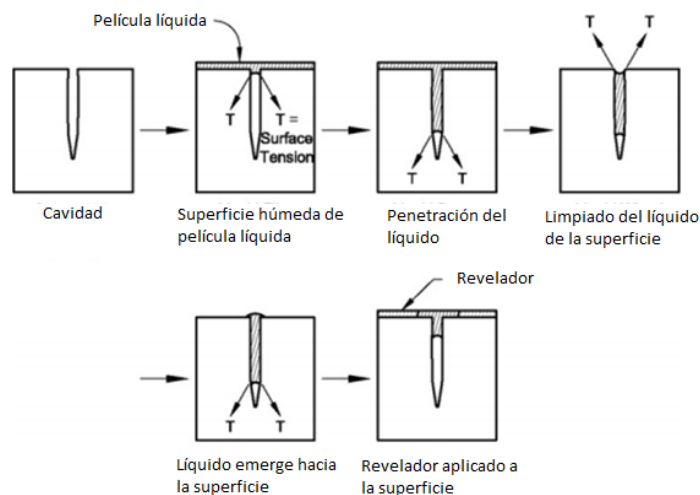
Principios físicos en la inspección por tintas penetrantes [27]
